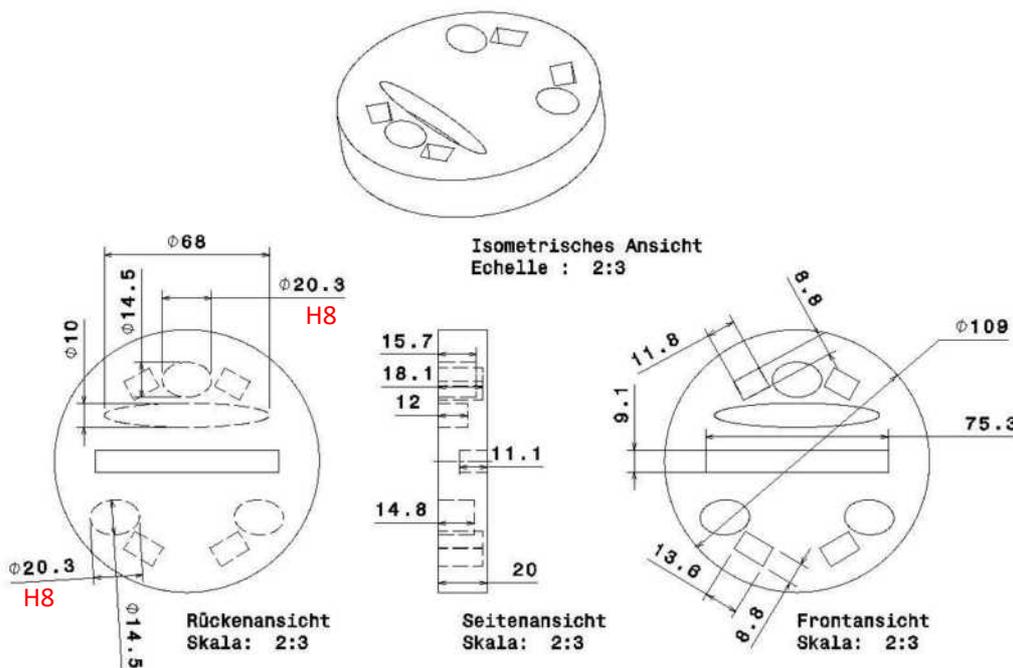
Element 9 (2D-Zeichnung) mit Toleranzen
